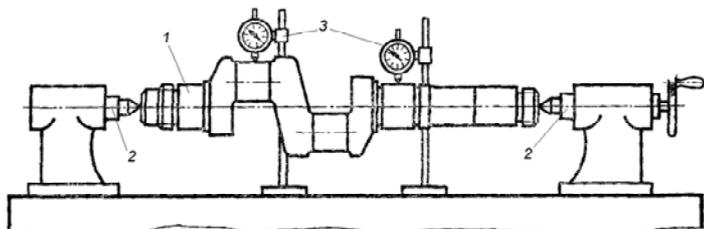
Схема проверки стоечным индикатором коренных и шатунных шеек вала, установленного в центрах:
